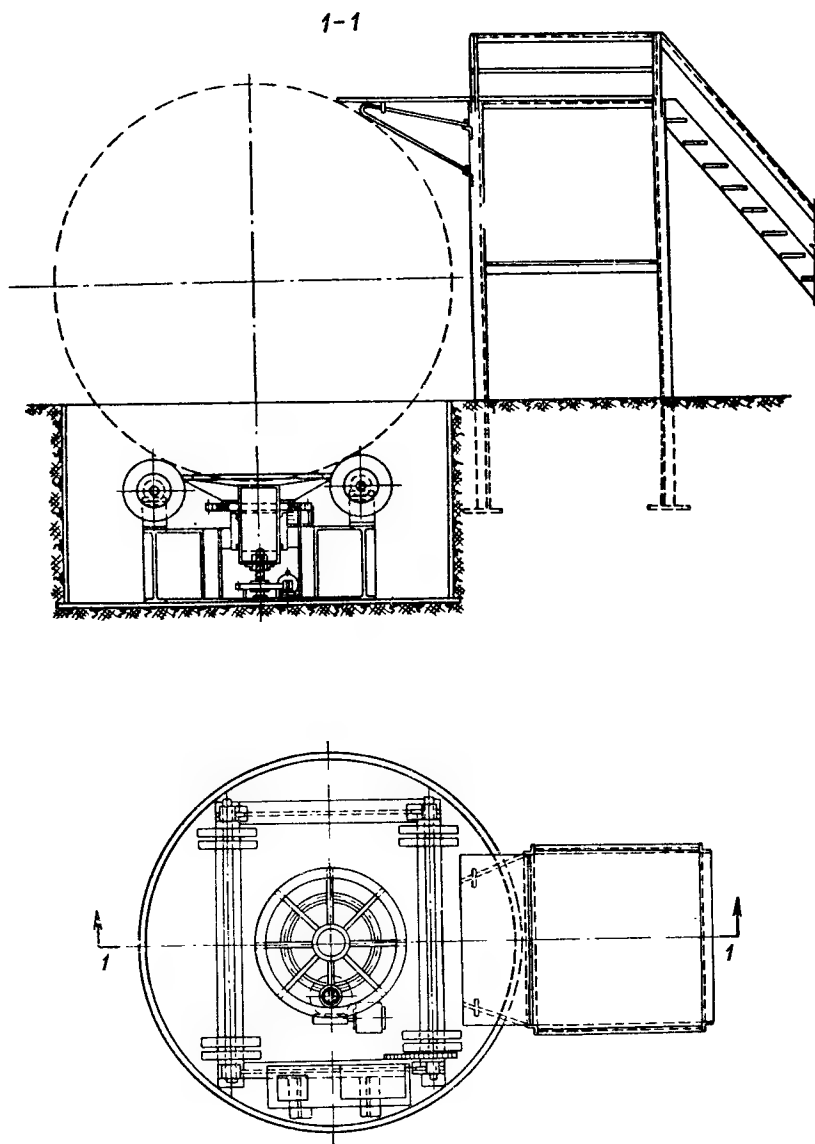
Роликовый стенд для автоматической сварки полушаровых днищ
